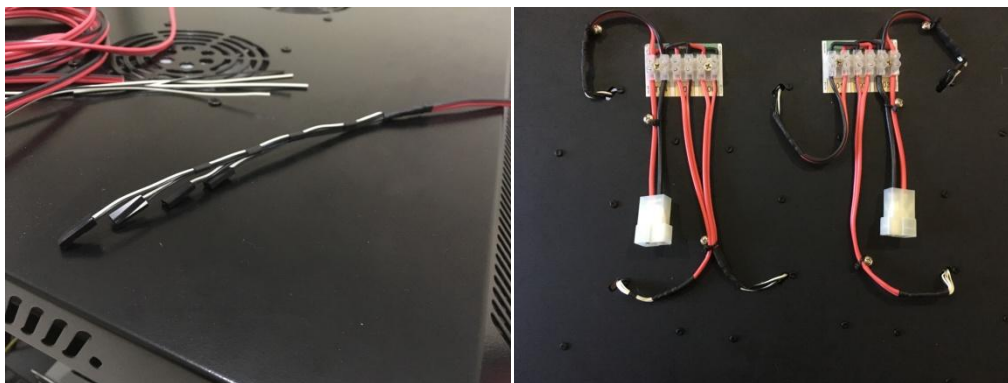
Cables de Alimentación. Fuente: Elaboración propia.
